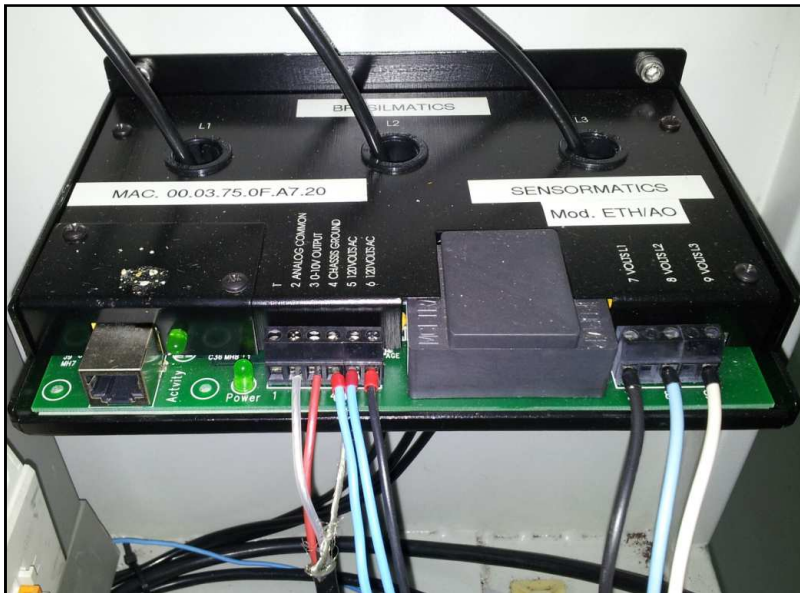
Fixação do sensor UPC-E no painel da máquina CNC
